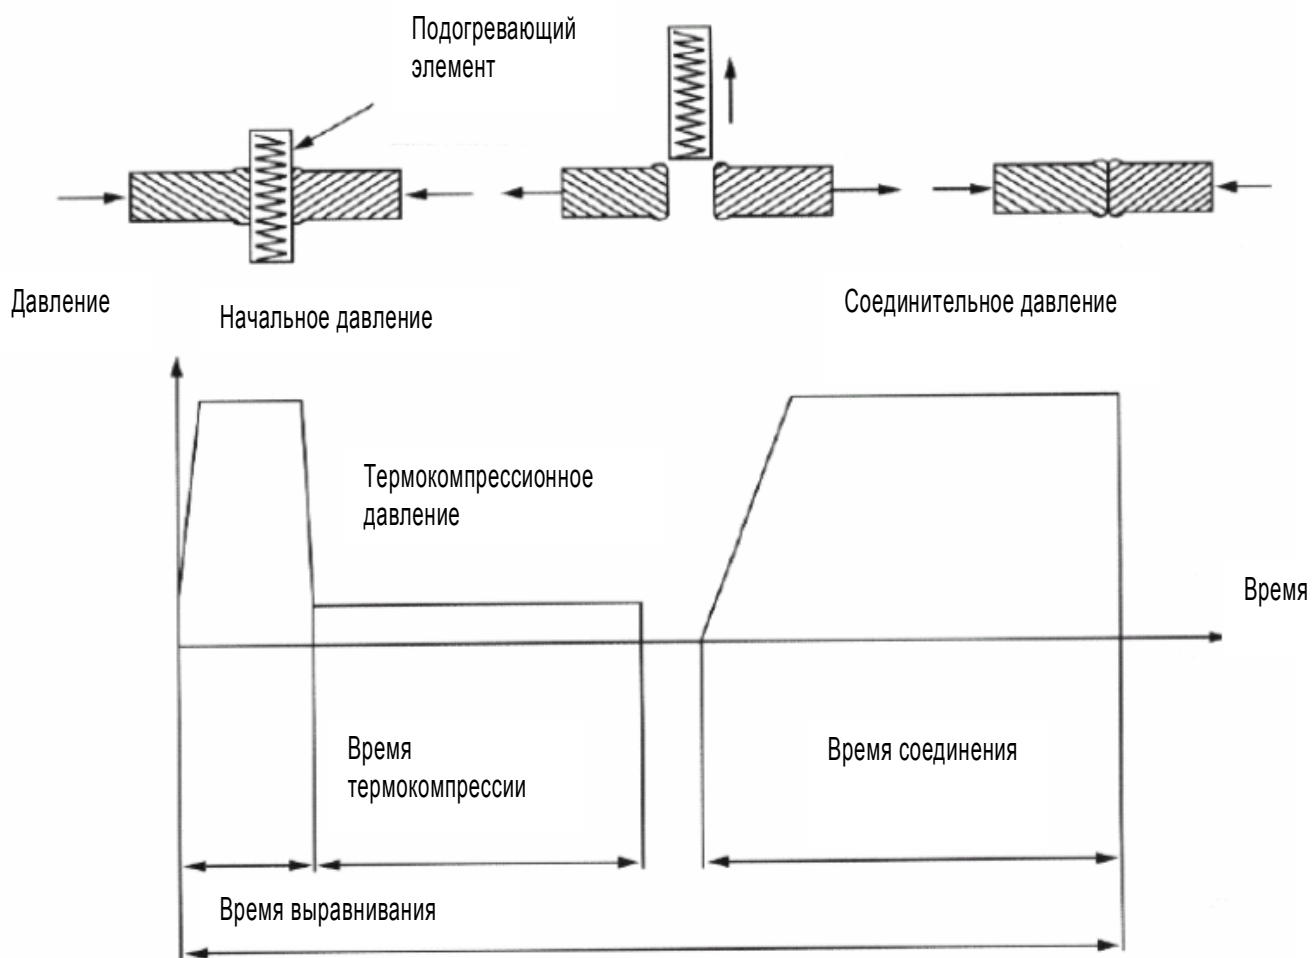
Схематическое изображение сплошной сварки с подогревающим элементом
